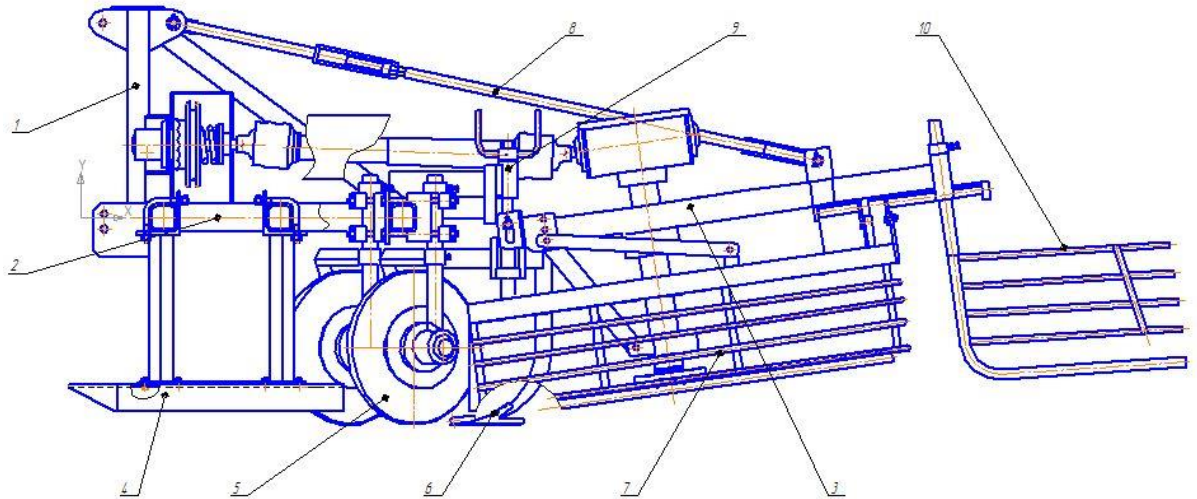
Схема модернізованого копача АЗБ-6 (вид збоку): 1 – навісний пристрій; 2 – рама передня; 3 –рама задня; 4 – лижа; 5 – диск викопуючий; 6 –лапа; 7 –решітка (дека) з паралельних прутків; 8 – регулюєма тяга; 9 – гвинтовий механізм; 10 – решітка валкоутворювача
